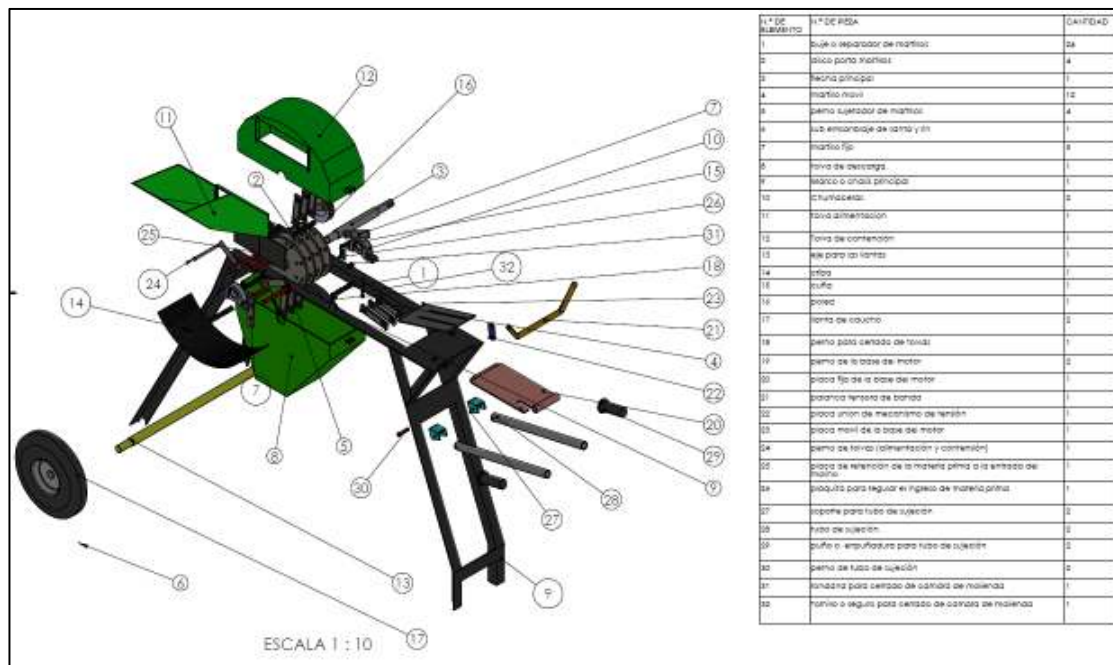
Ensamblaje general con vista explosionada de todos los componentes.
